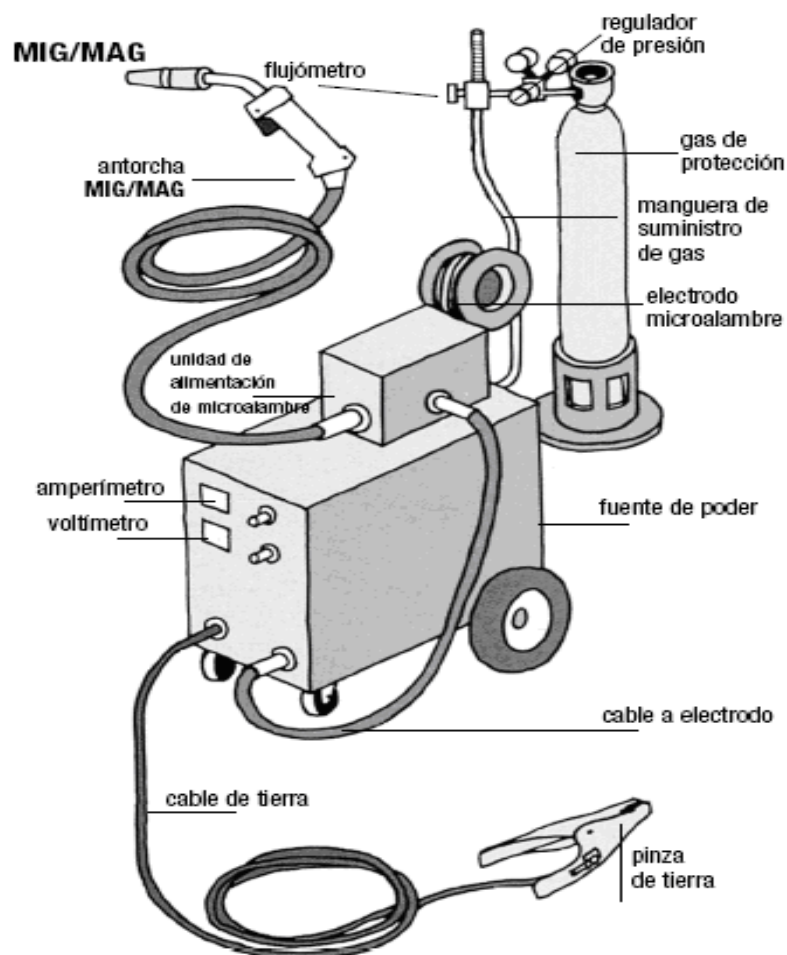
Circuito de soldadura para el proceso GMAW
